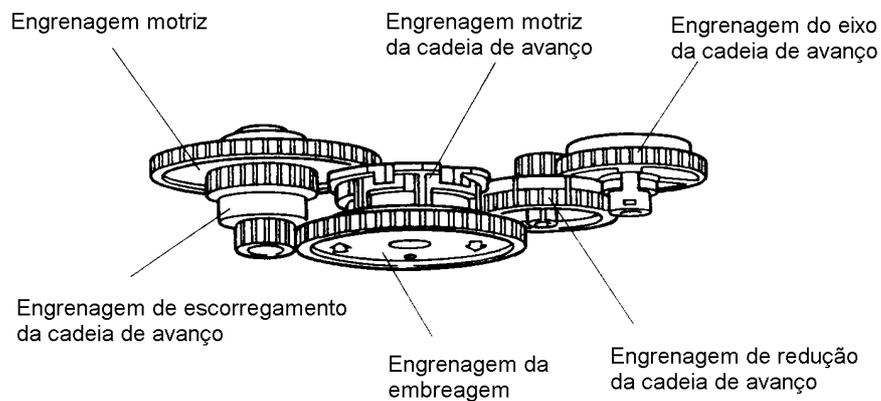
Cadeia de Engrenagens do Avanço de Papel
